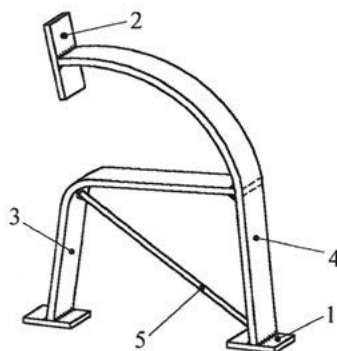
Blech-Kunststoff-Baugruppe für Hängeschrankbefestigung [45]
